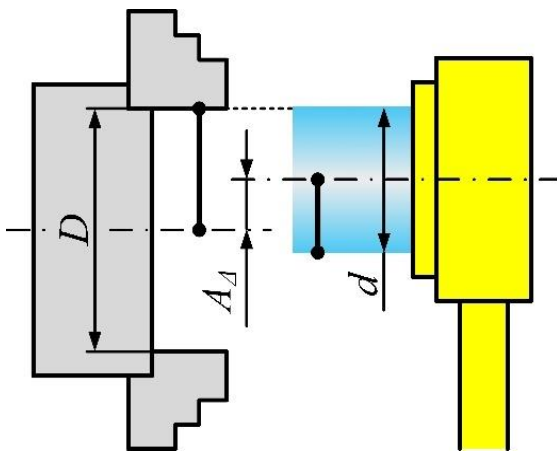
Схема встановлення заготовки у самоцентруючий патрон верстата
